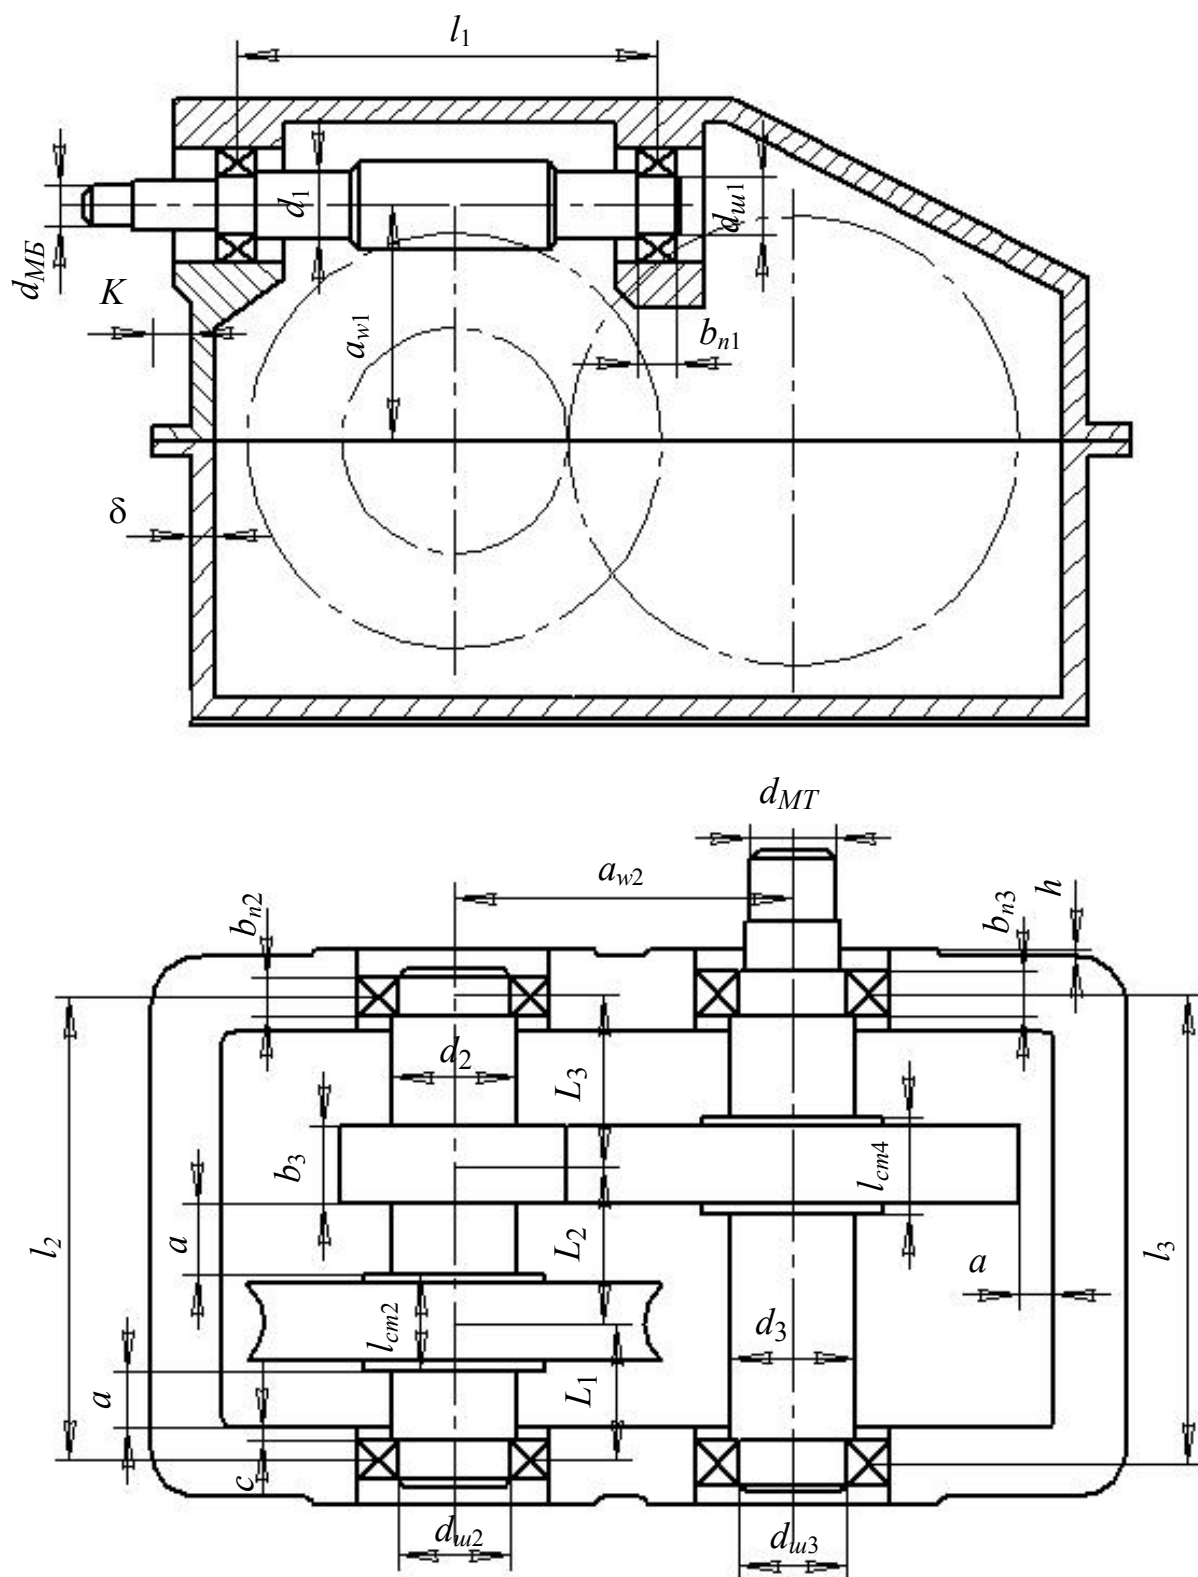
Эскизная компоновка червячно-цилиндрического двухступенчатого редуктора с верхним расположением червяка
